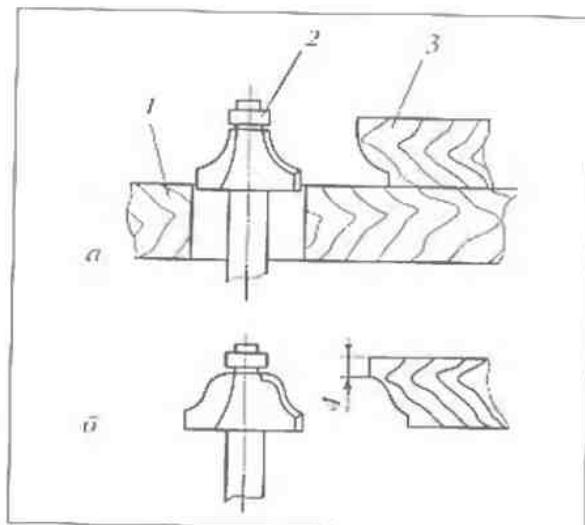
Фасонная обработка кромок: а - на фрезерном станке; б - фрезой оптимального профиля; 1 - рабочий стол; 2 - подшипник-ограничитель фрезы; 3 - обработанная деталь
